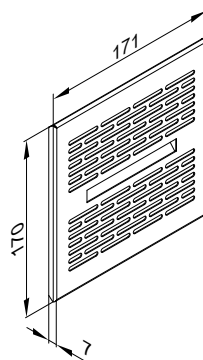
Декоративная крышка для выпуска воздуха на дальнейшее расстояние, проход для воздуха на стене и перекрытии
